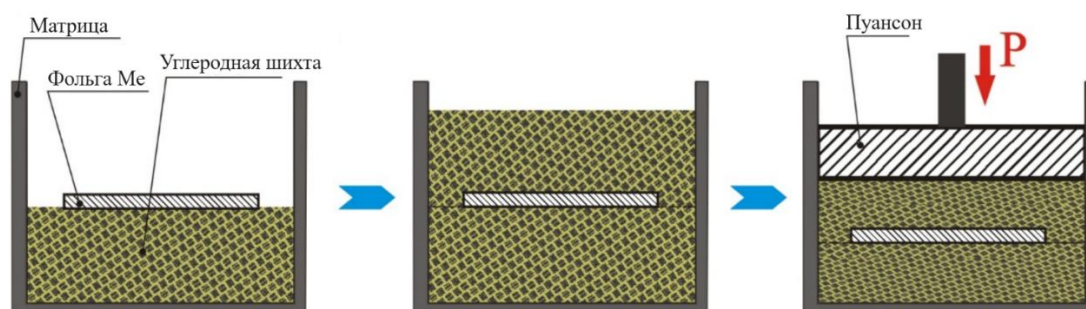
Схема получения углеродной пористой заготовки с внедренной в ее объем металлической фольгой.
